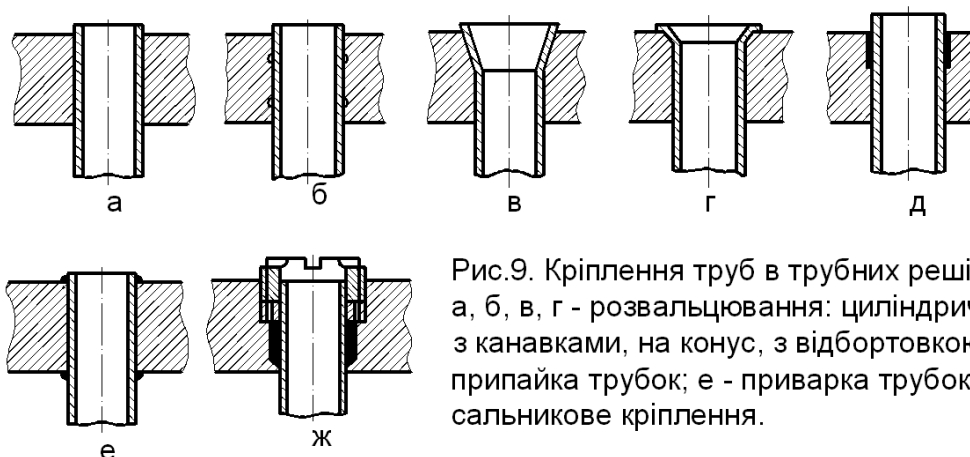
Кріплення труб в трубних решітках: а, б, в, г - розвальцювання: циліндричне, з канавками, на конус, з відбортовкою; д - припайка трубок; е - приварка трубок; ж - сальникове кріплення.
